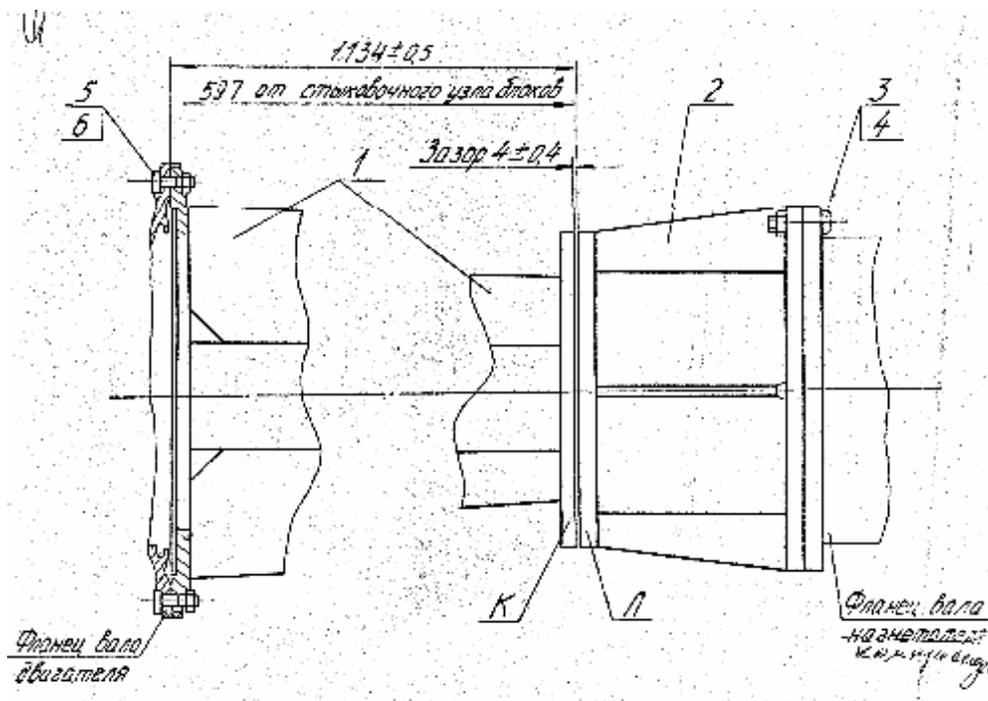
Монтаж приспособлений-катушек на фланцы валов двигателя и компрессора
